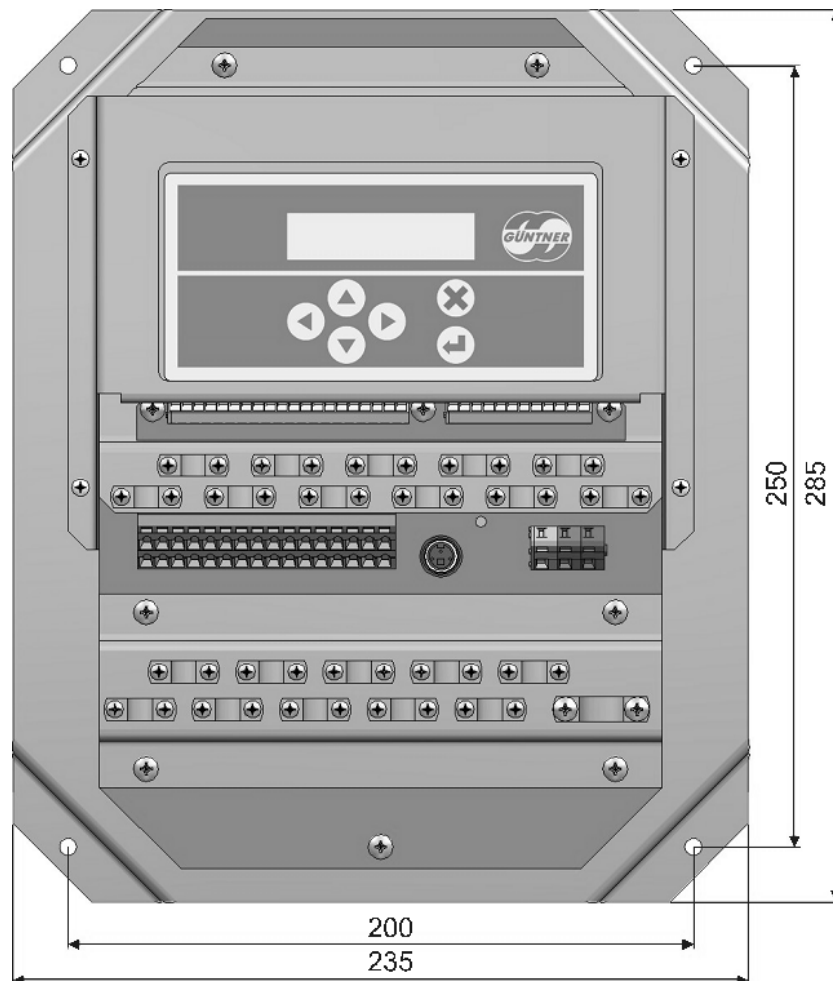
Dimensões de caixa GMM EC 01 / 04 / 08 (.1) UL
